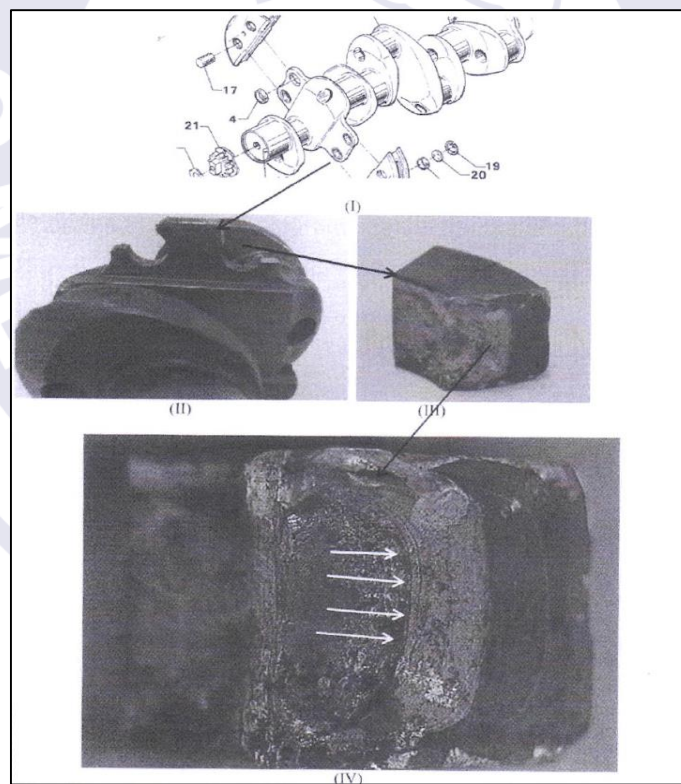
(I) visão explodida dos componentes do virabrequim e seus elementos.
